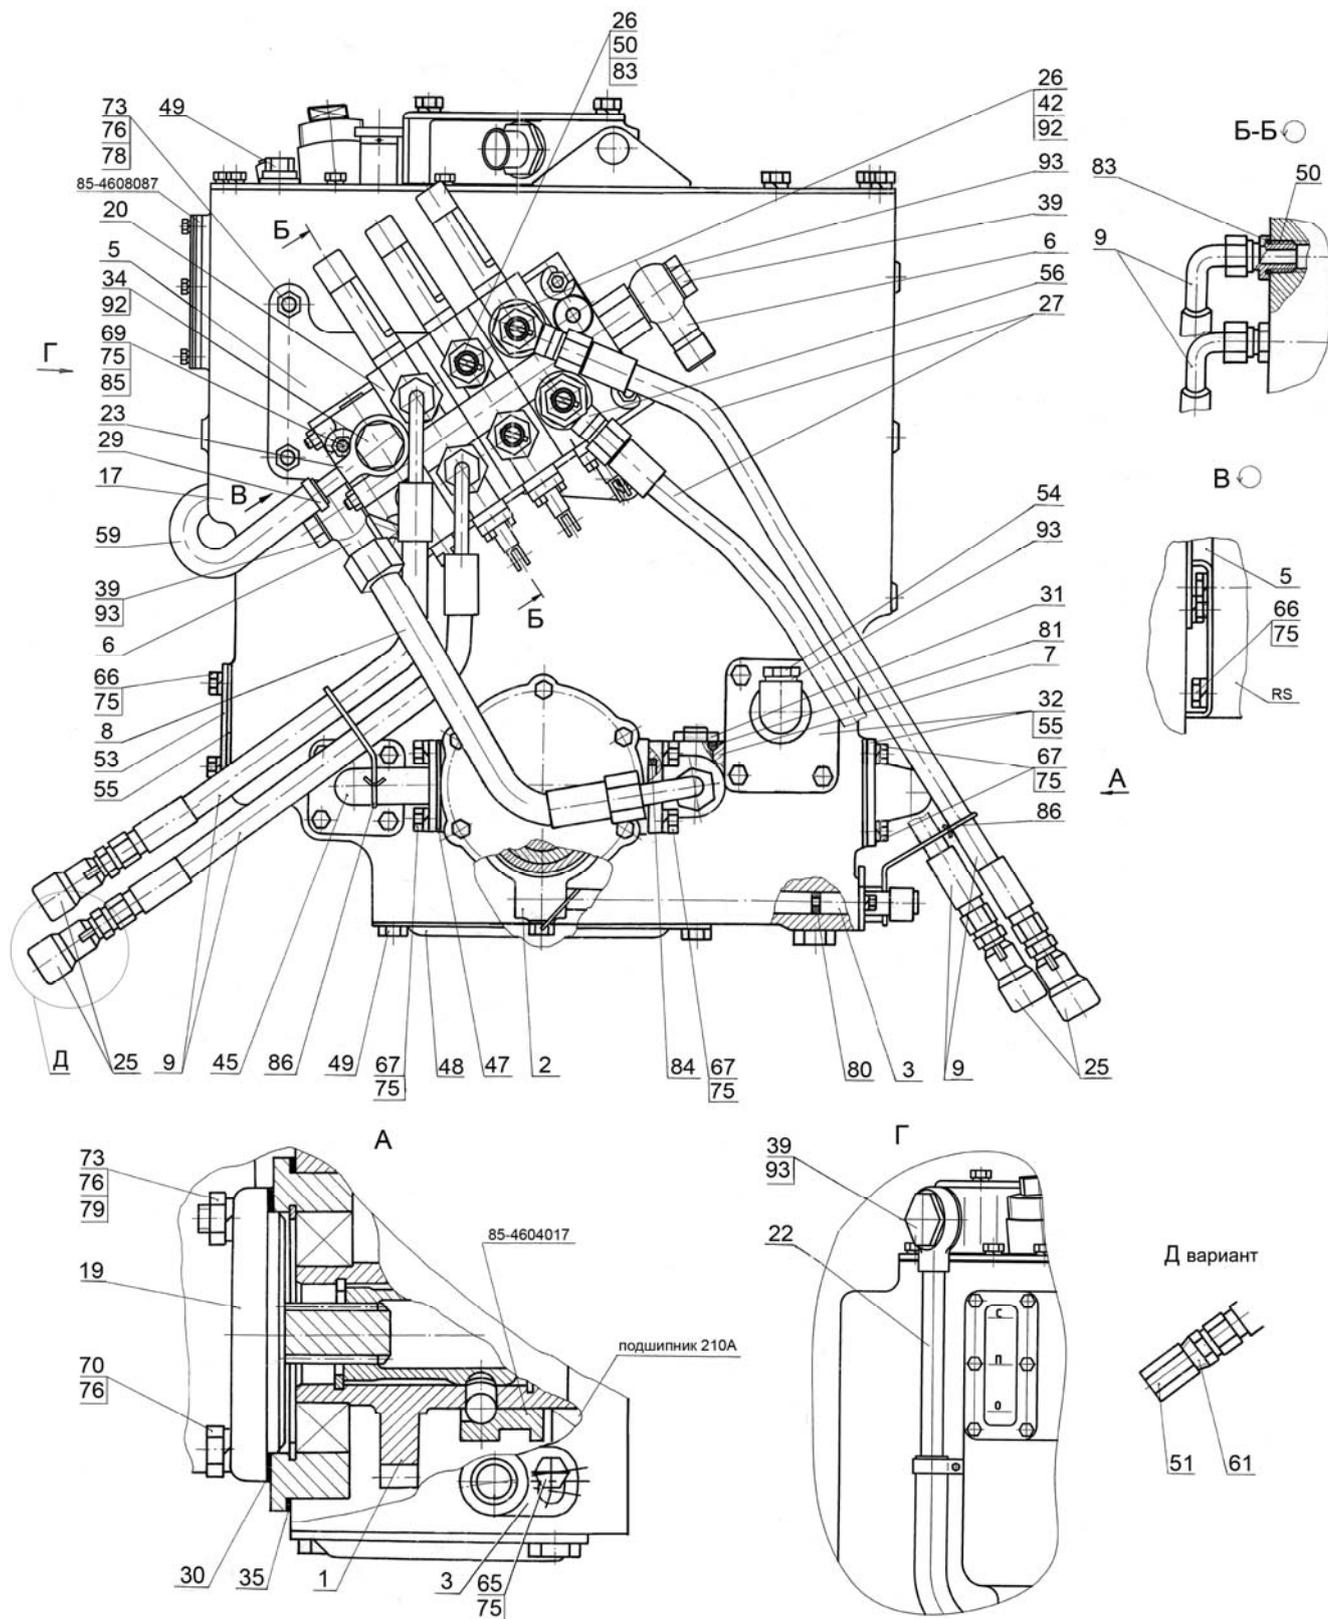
Корпус гидросистемы 952-4600015-08
